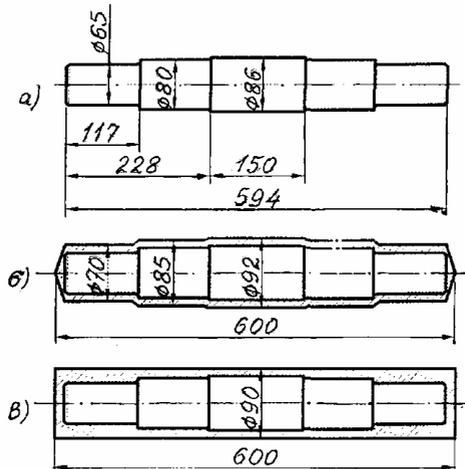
Вал ступенчатый: а – готовая деталь; б – штампованная поковка; в – заготовка из горячекатаного проката
